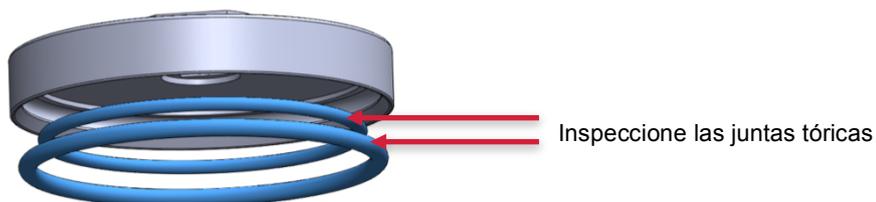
Desmontaje del retenedor e inspección de las juntas tóricas
